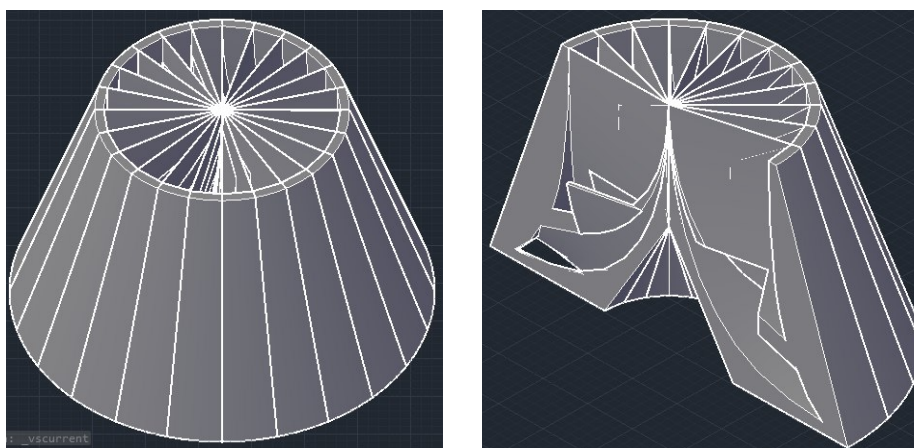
Конструкция насадки для равномерного распределения воздушного потока на выходе вентиляционной шахты
